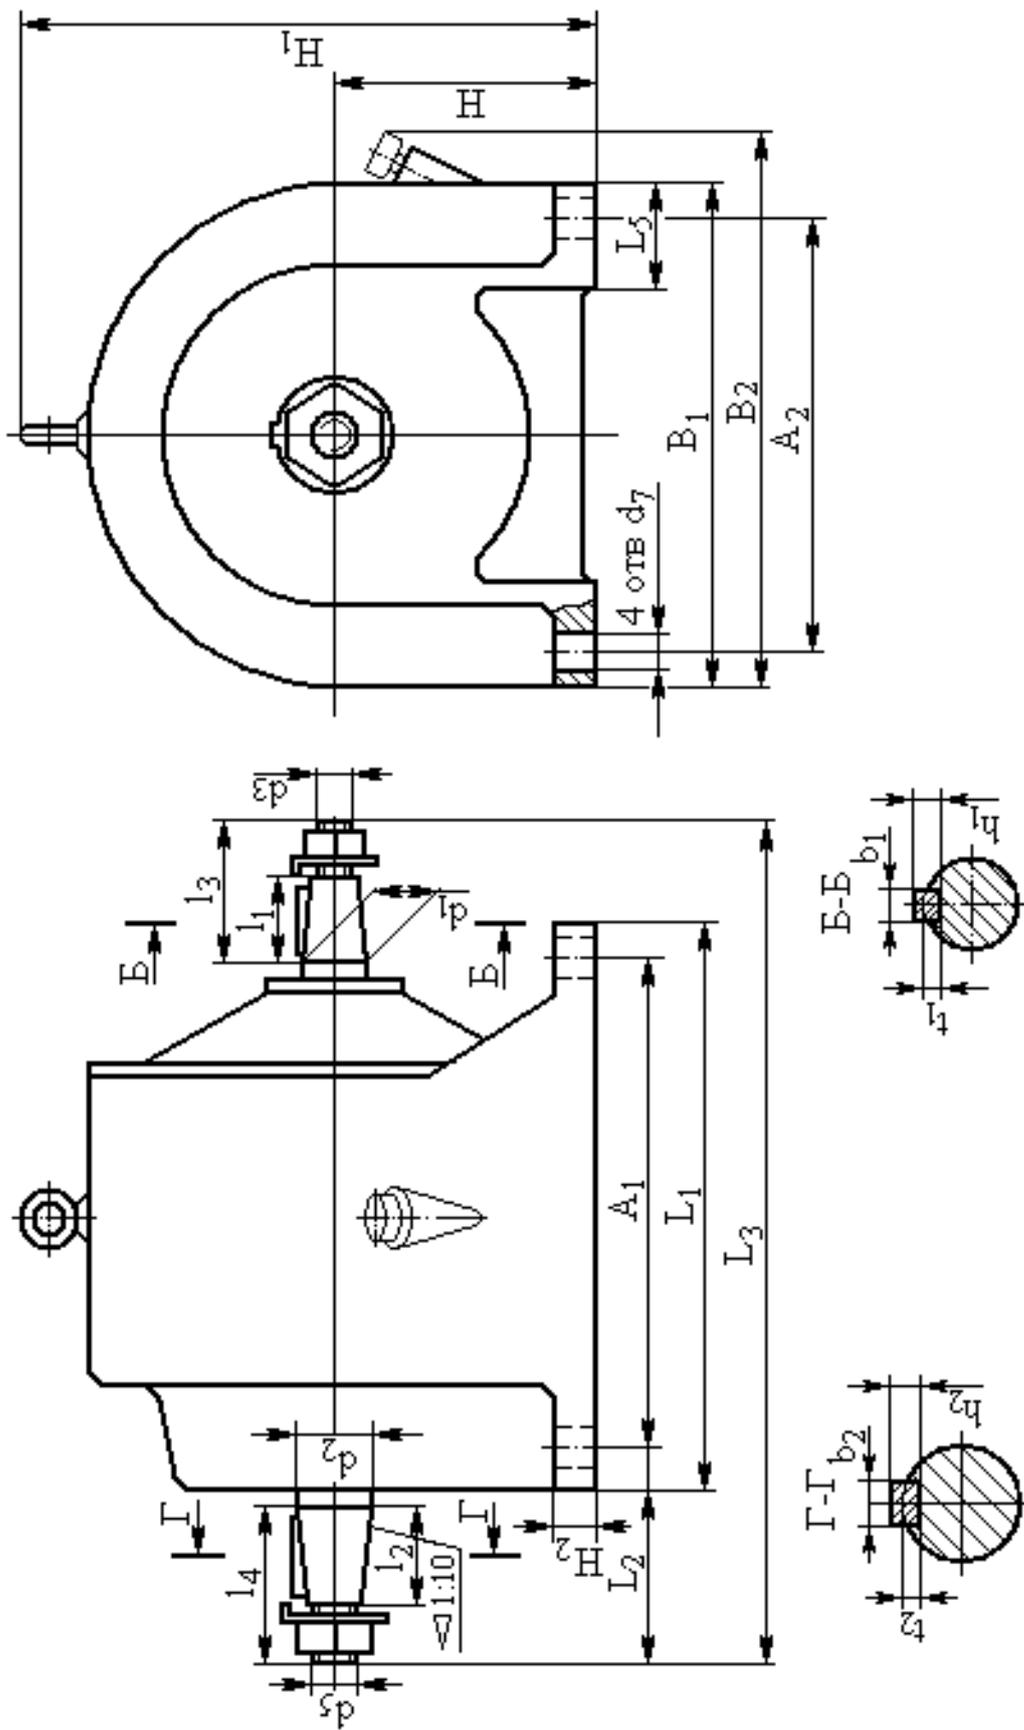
Планетарный зубчатый одноступенчатый редуктор типа Пз
